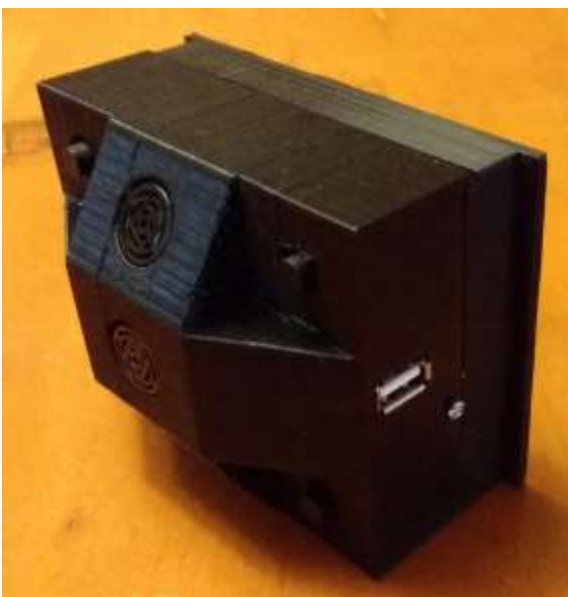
Montaje de la placa USB en la parte lateral derecha del dispositivo
